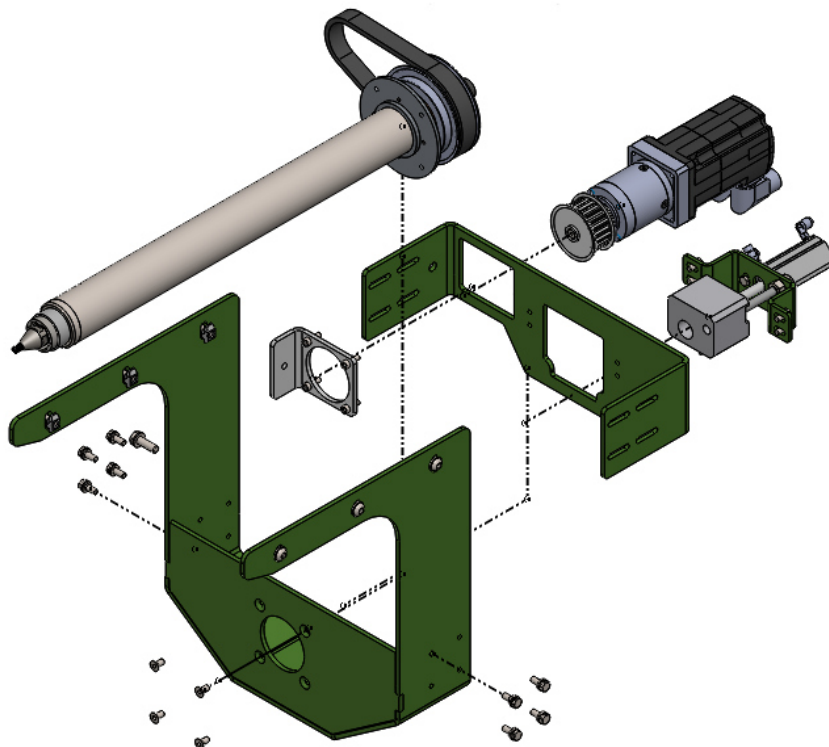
Vista explodida do conjunto "Suporte da Bobina"
